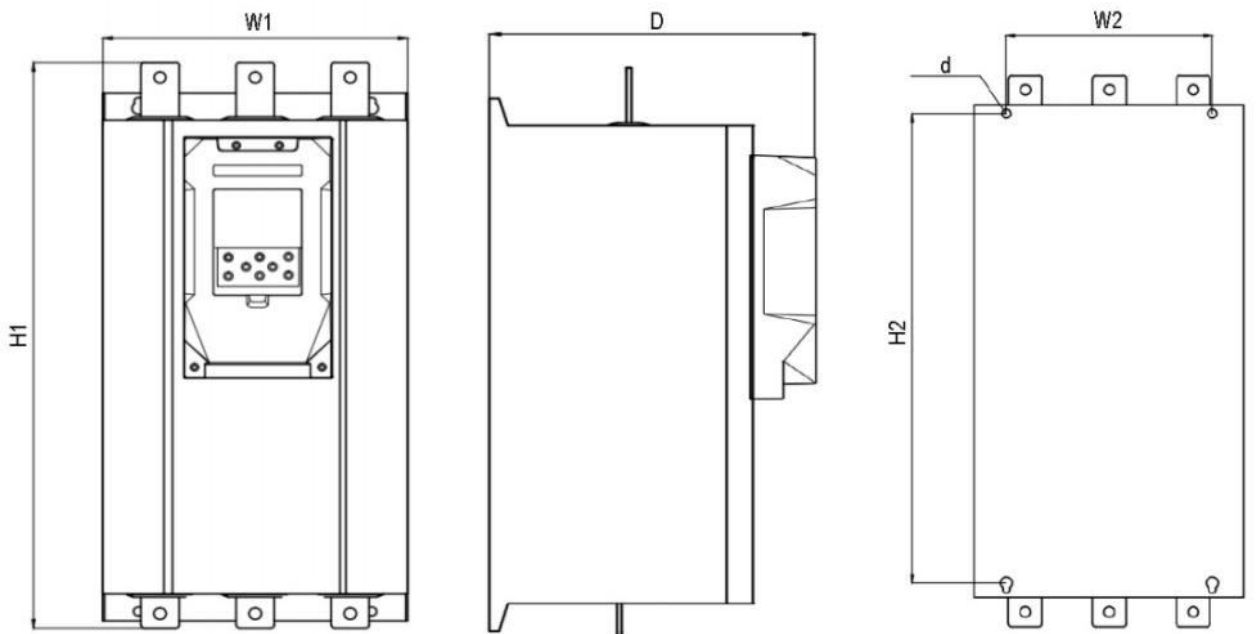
Габаритные и установочные размеры RR2-RR3
